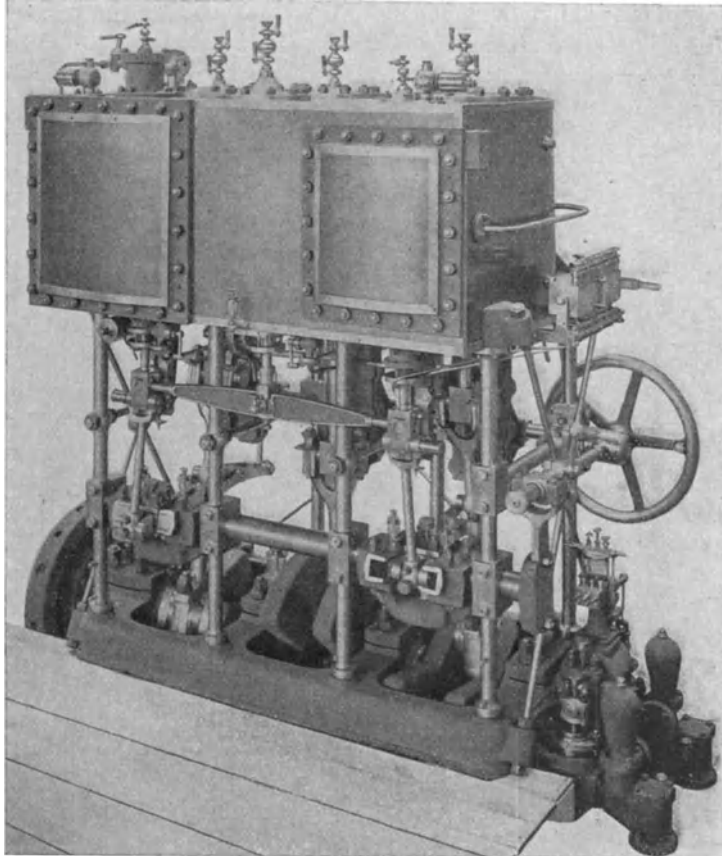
Leichte Dreifach-Expansionsmaschine für Schraubenschiffe mit getrennt liegender Kondensation, 250 PSi (gebaut von Escher Wyss & Cie., Zürich).
